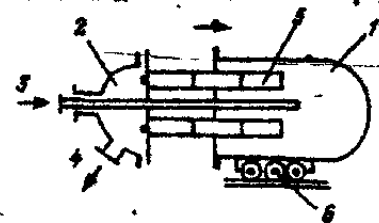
Вариант (а) конструктивного решения для патронного фильтра с горизонтальным расположением фильтроэлементов при фильтровании суспензии без образования осадка (осветлительное фильтрование): 1 — съемный корпус; 2 — камера для фильтрата; 3 — штуцер для ввода суспензии; 4 — штуцер вывода фильтрата; 5 — патронные фильтроэлементы; 6 — устройство для перемещения корпуса
